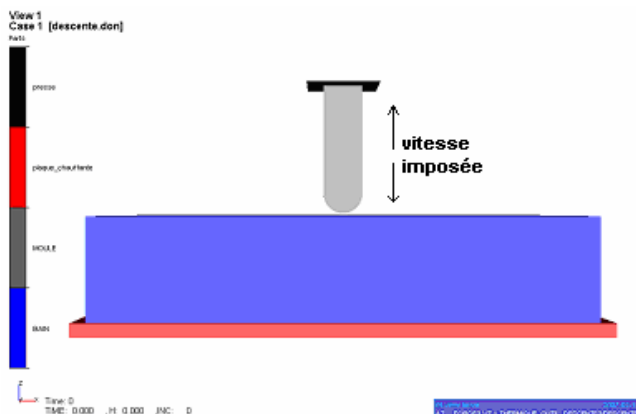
Ensemble des outils (plaque chauffante, moule et presse) et bain modélisés sous Forge
